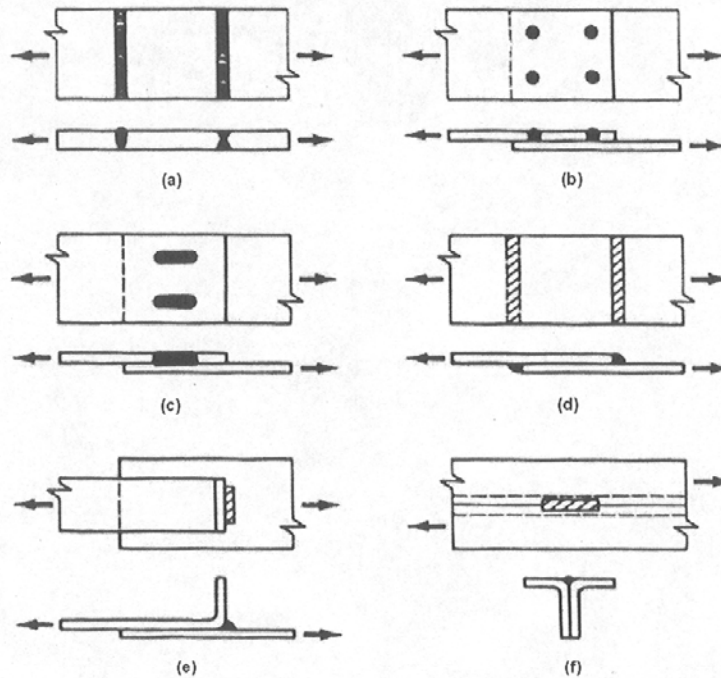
Tipos de soldaduras de arco (1). (a) Soldaduras de penetración en juntas de frente; (b) soldaduras de punto; (c) Soldaduras de costura; (d) Soldaduras de filete; (e) Soldaduras de penetración abierta de bisel en "J"; (f) Soldaduras de penetración abierta en "V".
